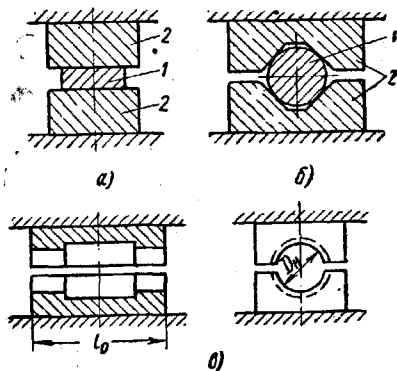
Детали сварочного контура стыковых машин.
